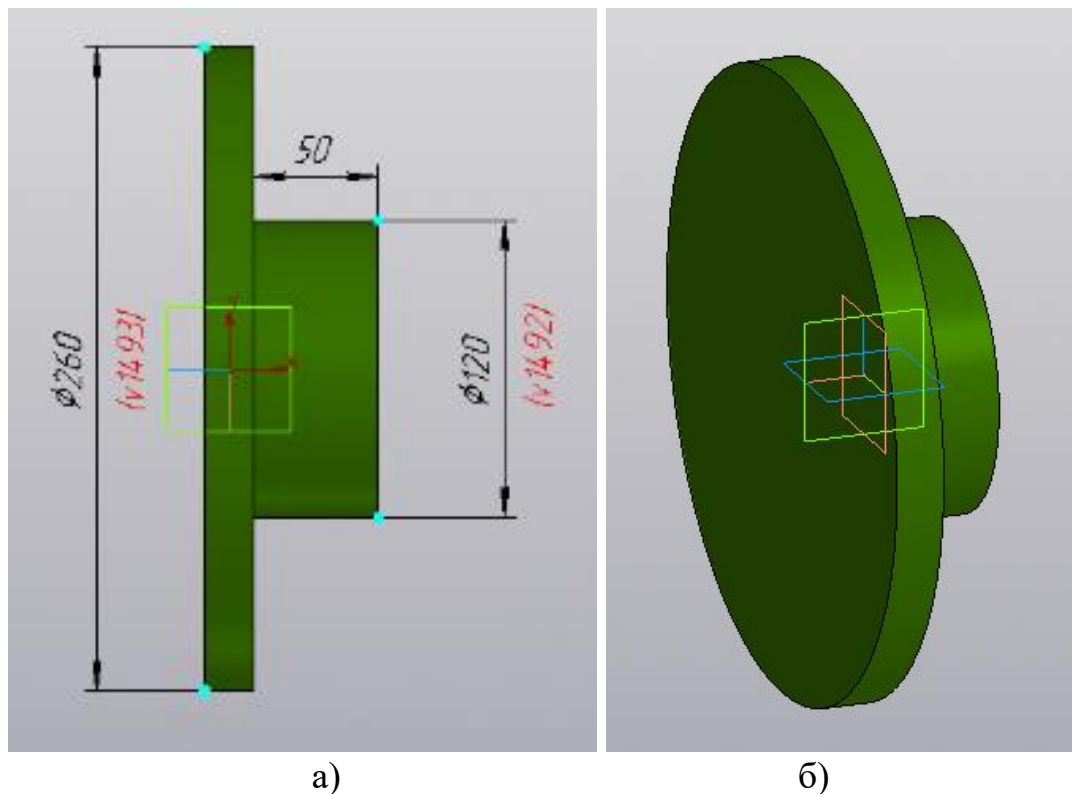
(а, б) 3д модель заготовки після операції проточування
